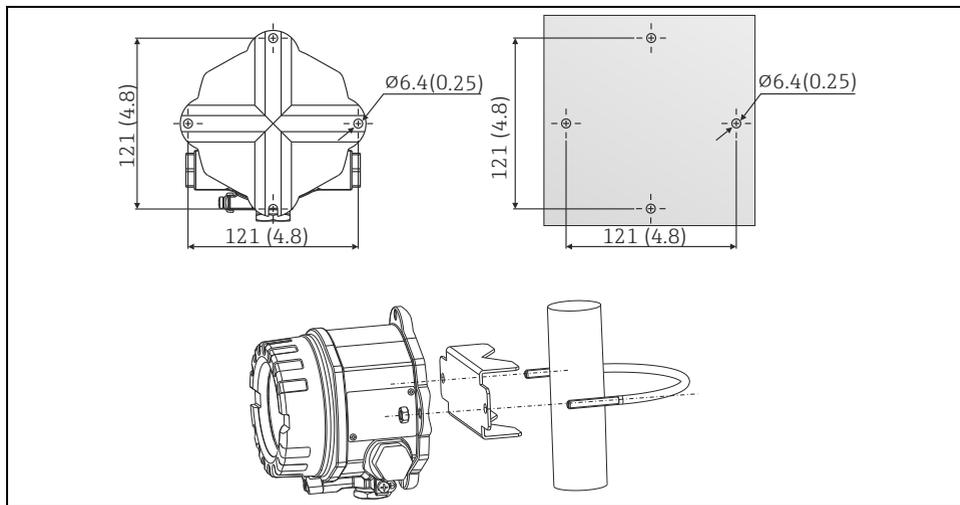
Montage direct sur mur ou sur colonne (dimensions en mm (in))
